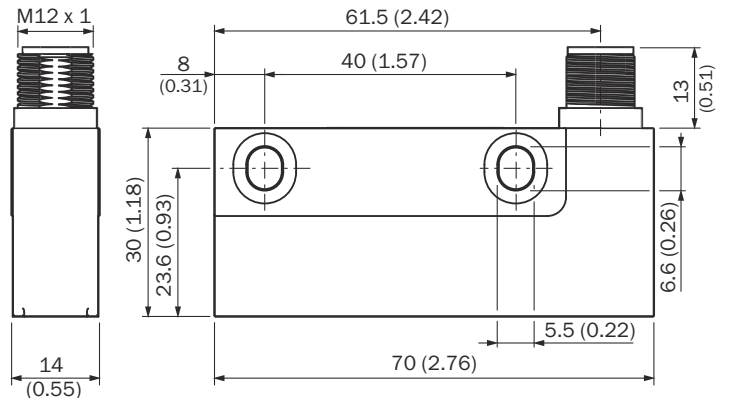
Plan coté TTK70S avec connecteur mâle M12, (dimensions en mm)
